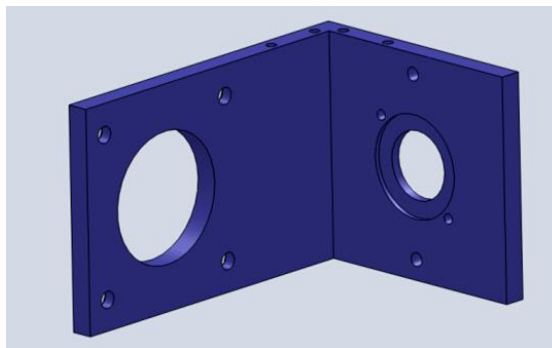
Diseño CAD de eslabonamientos de prototipo.
